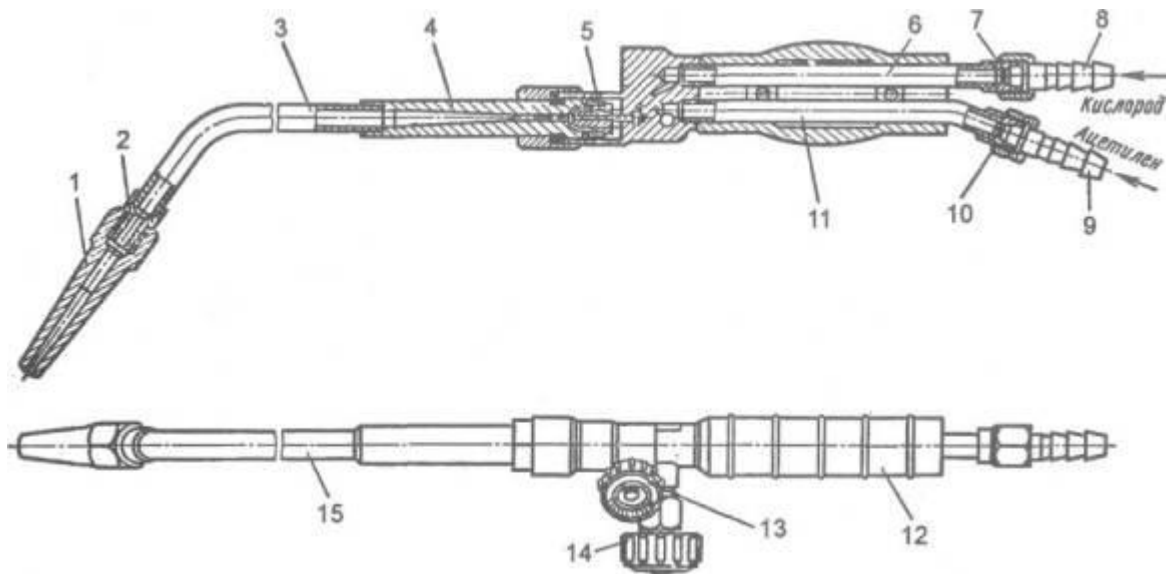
Пальники зварювального типу Г-2-02 и Г-3-02:
